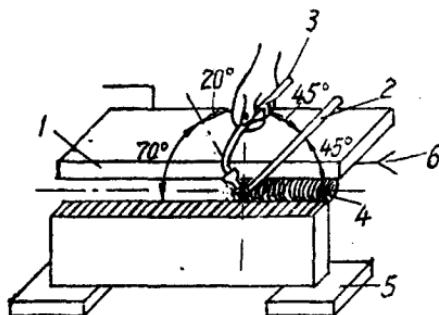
气焊焊枪、焊条与工件之间的角度：
